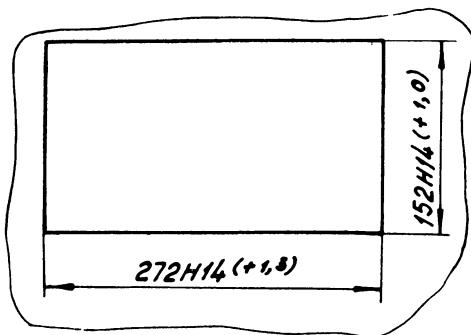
Габаритный чертеж промежуточных преобразователей ППС и ППЧ
